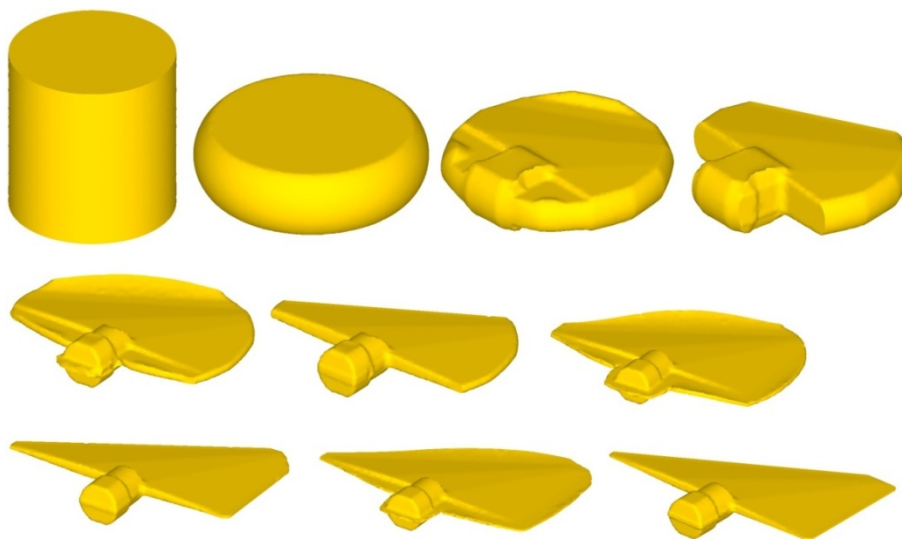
Изменение геометрии заготовки по переходам производственного процесса горячей объёмной штамповки поковки
